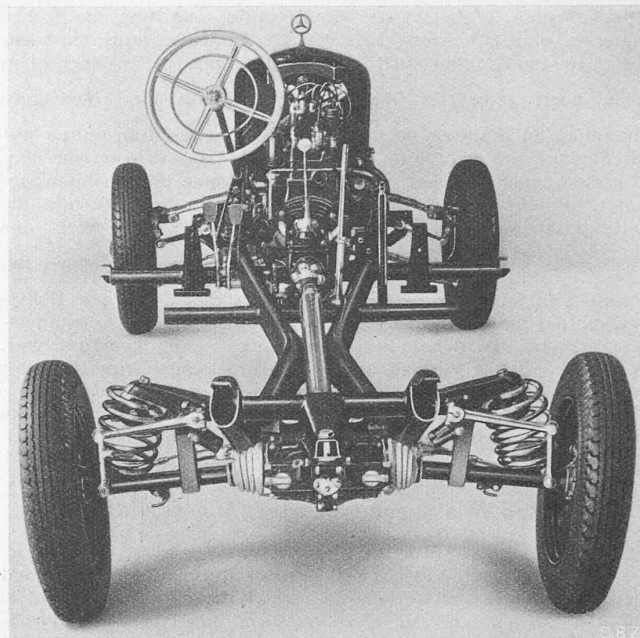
Chassis mit Einzelfederung aller vier Räder (Vollschwingachs-Chassis Mercedes-Benz 170 V, 9 PS). Rahmen modernster Ausführung, in X-Form geschweisste Träger von rechteckigem Profil. Vorn zwei übereinanderliegende Blattfedern, hinten Pendelachsen mit Spiralfedern
